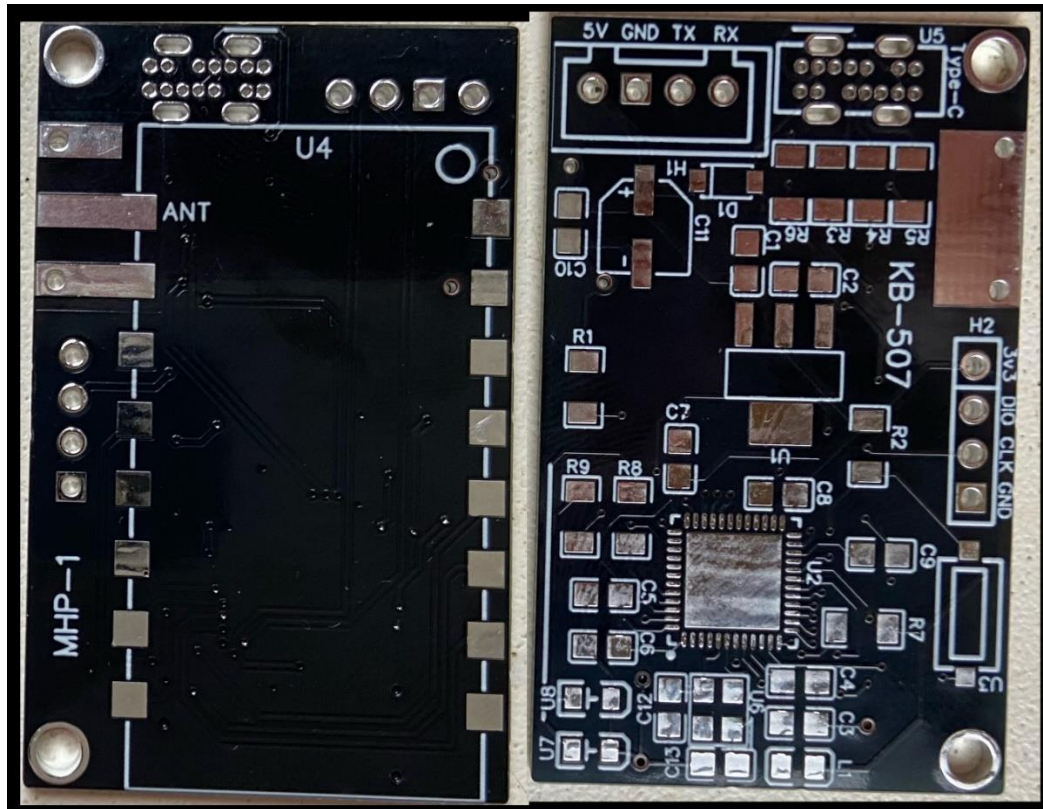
Внешний вид изготовленной платы приемопередатчика БПЛА.
